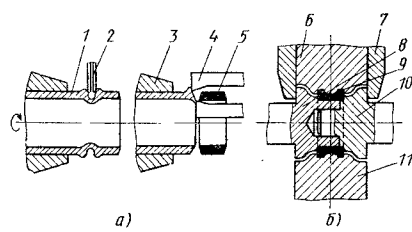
Схема технологического процесса раскатки обоймы подшипников качения: 1 — труба (заготовка); 2 — диск; 3 — зажим; 4 — резец; 5 — заготовка; 6 — раскатной подвижный ролик; 7 — ограничивающие реборды; 8 — передняя оправка; 9 — обойма; 10 — задняя оправка; 11 — раскатной неподвижный ролик
